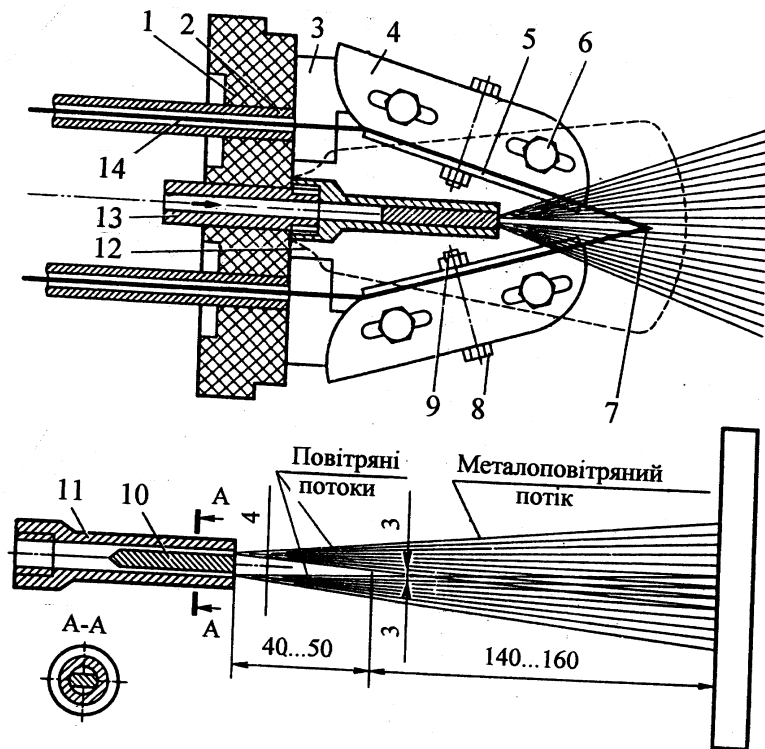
Розпилювальна головка із двоканальним повітряним соплом: а – конструктивна схема; б – схема нанесення покриття; 1 – панель; 2 – напрямна трубка; 3 – шина; 4 – планка напрямна; 5 – пружина; 6, 8 – болт; 7 – дуга; 9 – гайка; 10 – перегородка повітряного сопла; 11 – повітряне сопло; 12 – екран захисний; 13 – повітряпровід; 14 – дріт для напилення
